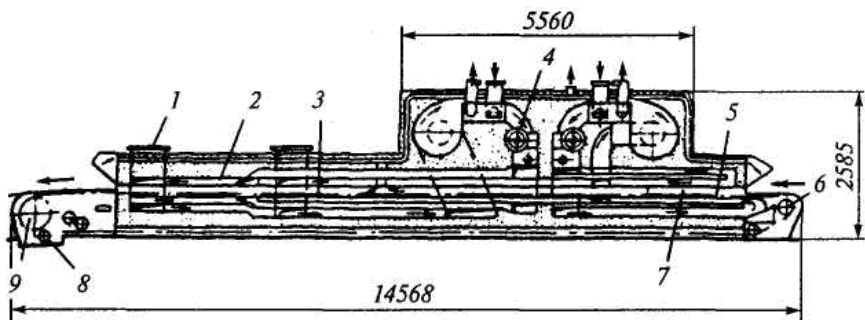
Піч ПХС-25М; 1 – витяжний канал; 2, 3 – верхній і нижній обігрівальні канали; 4 – топка; 5 – стрічкова черінь; 6 – натяжний барабан; 7 – фартук; 8 – щітка; 9 – привідний барабан.
